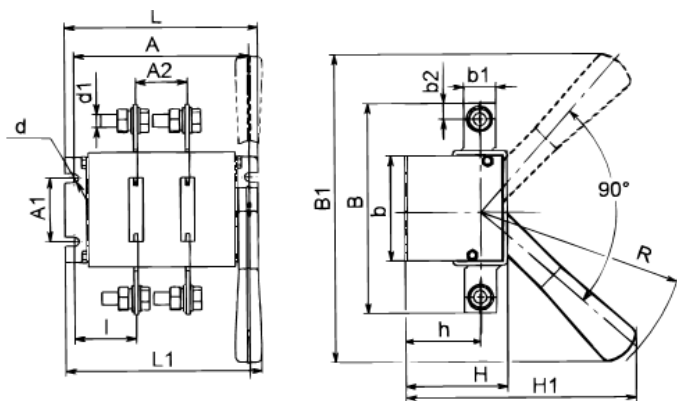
Б Выключатель-разъединитель на одно направление двухполюсный с боковой рукояткой
